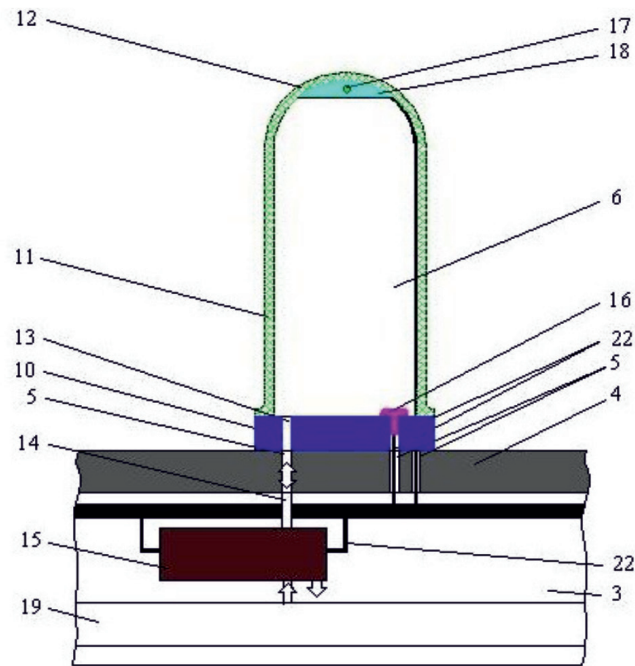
Общий вид исполнительного элемента в виде пневматической камеры
